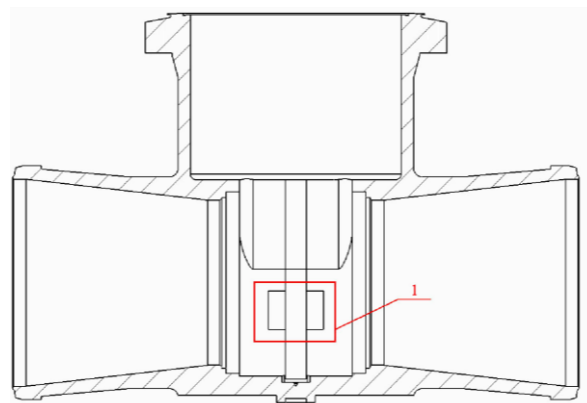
Сгенерированный по трехмерной модели чертеж корпуса.
